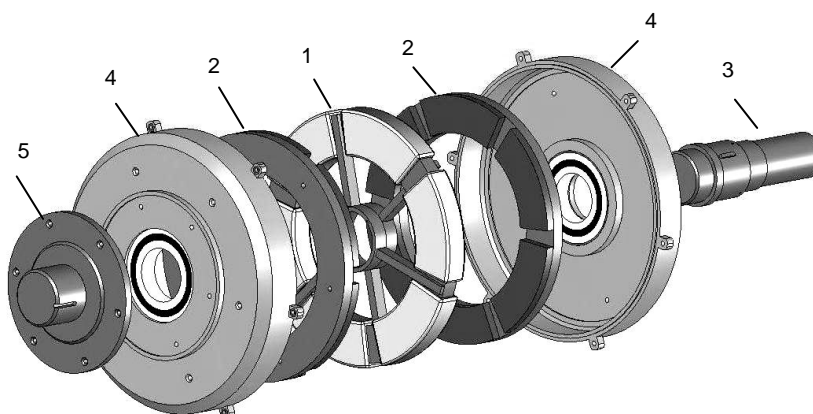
Основные узлы генератора: 1 – тороидальный статор с кольцевой обмоткой; 2 – индукторы с постоянными магнитами; 3 – неподвижный вал; 4 – подшипниковые щиты; 5 – крышка-фланец, принимающая вращение от ветроколеса или редуктора
